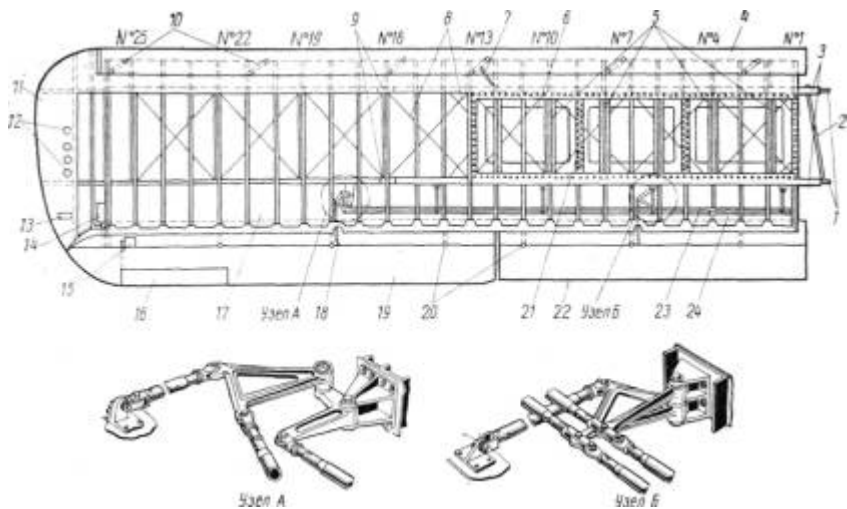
Схема каркаса левой отъемной части верхнего крыла: 1 — узлы крепления крыла к фюзеляжу; 2 — трубчатый раскос; 3 — лонжероны; 4 — предкрылок; 5 — ложементы топливных баков; 6 — топливные баки; 7 — шнуровой амортизатор предкрылка; 8 — Внутрикрыльевые ленты-расчалки; 9 — узлы крепления бипланной стойки к крылу; 10 — качалки предкрылка; 11 — законцовка крыла; 12 — отверстия для облегчения; 13 — отверстия для монтажа и демонтажа тяг управления закрылком и элероном; 14 — весовой баланси́р элерона; 15 — электромеханизм УТ-6Д; 16 — триммер элерона; 17 — обшивка хвостовой части крыла; 18 — кронштейн крепления тяги управления элероном; 19 — элерон; 20 — кронштейны подвески элеронов и закрылков; 21 — крепление панелей топливных люков; 22 — закрылок; 23 — жесткие тяги управления закрылком; 24 — жесткие тяги управления элероном
